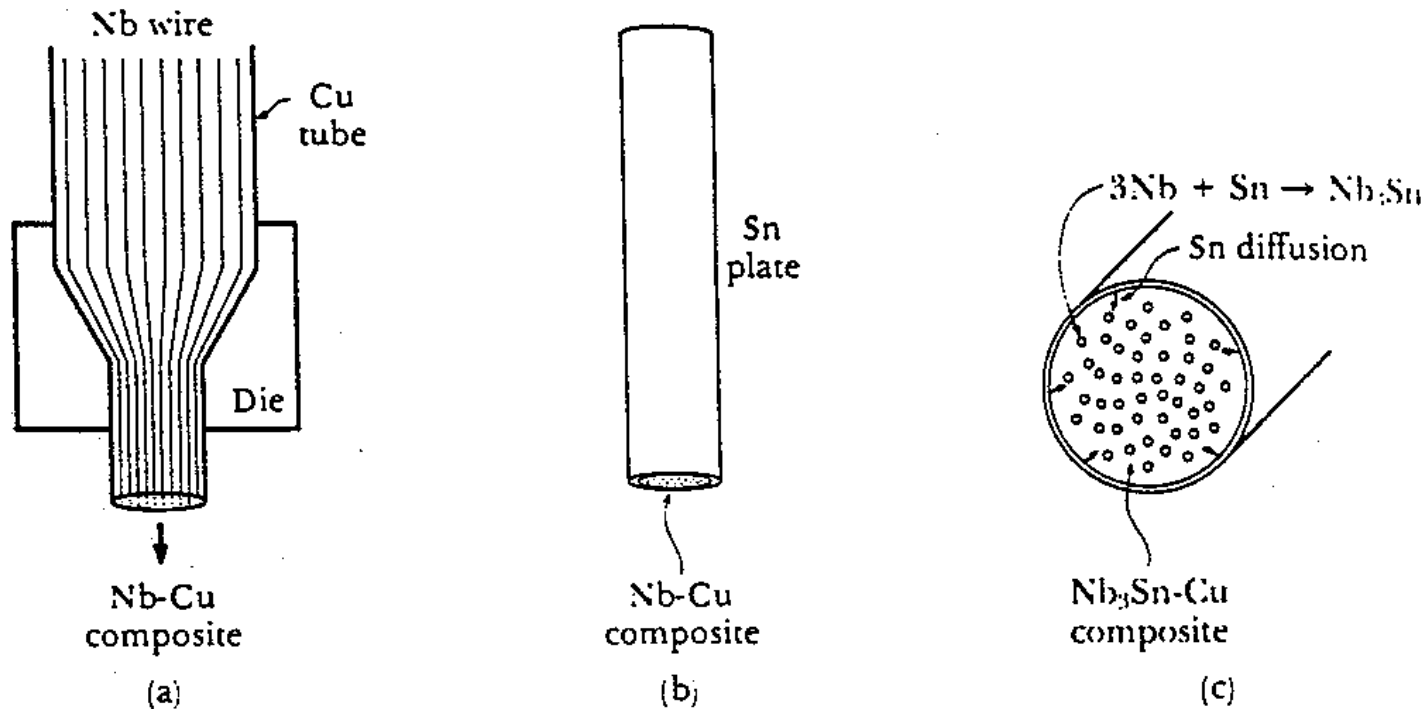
Procédé de fabrication de cables supraconducteurs.
